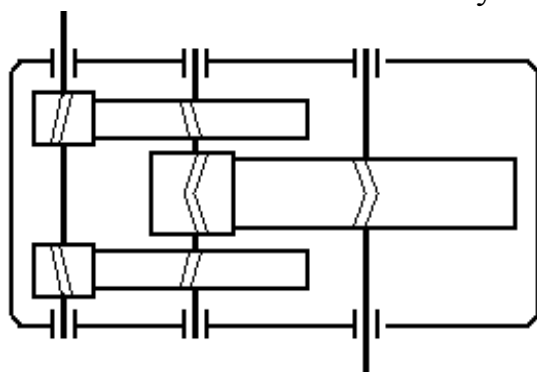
Цилиндрический двухступенчатый шевронный редуктор с раздвоенным потоком мощности
